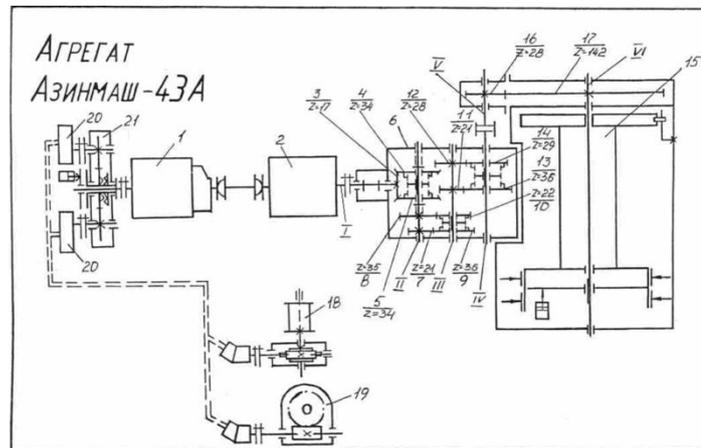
Кинематическая схема агрегата Азинмаш 43А
